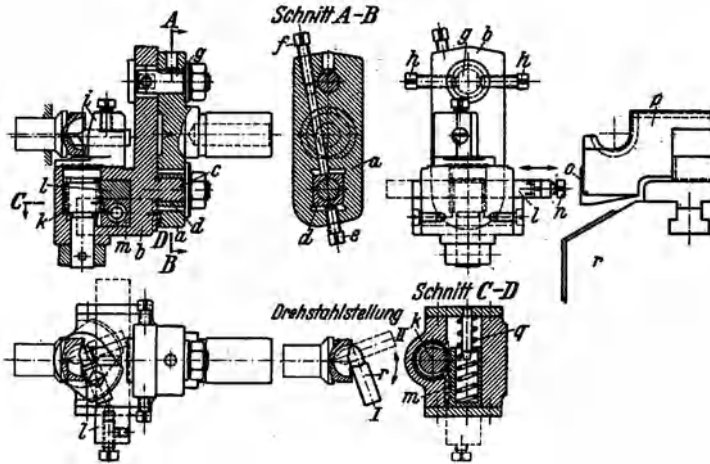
Kugeldrehwerkzeug im Revolverkopf zu Abb. 82.
